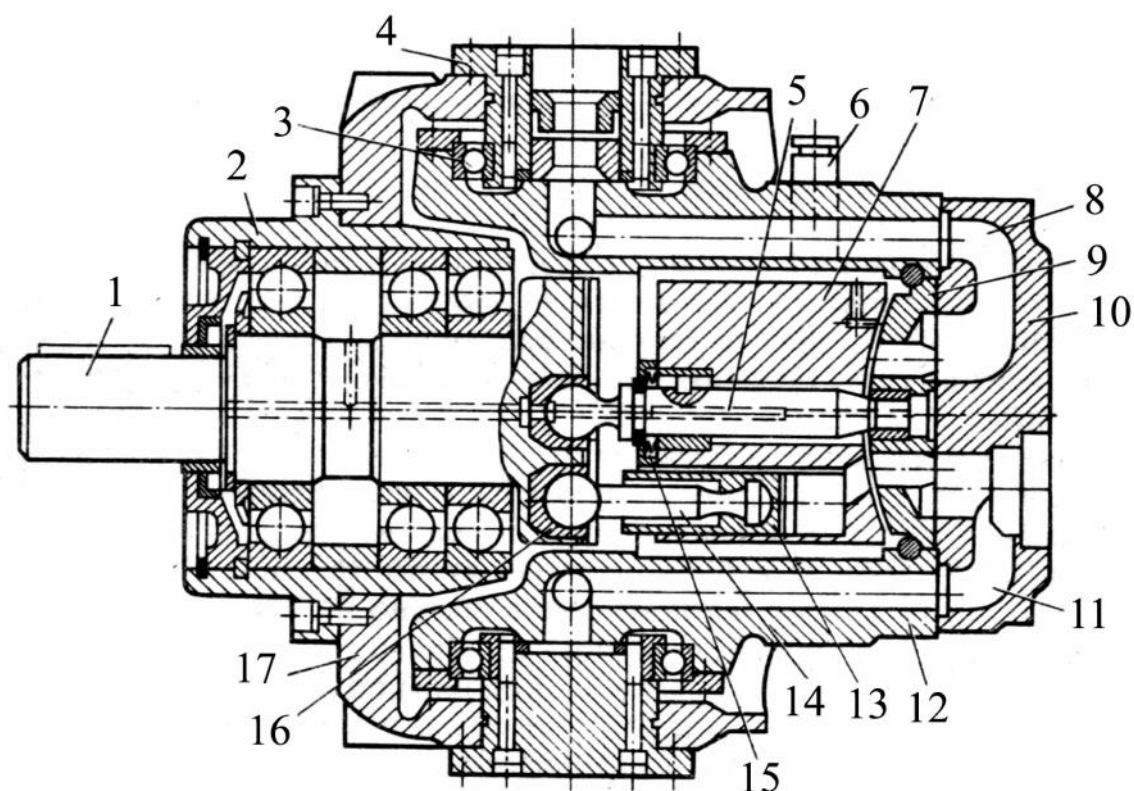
Аксиально-поршневой насос регулируемой подачи: 1 – вал; 2 – корпус; 3 – подшипники; 4 – цапфы; 5 – ось; 6 – палец; 7 – блок цилиндров; 8, 11 – каналы; 9 – распределительный диск; 10 – крышка; 12 – люлька; 13 – поршень; 14 – шатун; 15 – пружина; 16 – вкладыш; 17 – корпус
